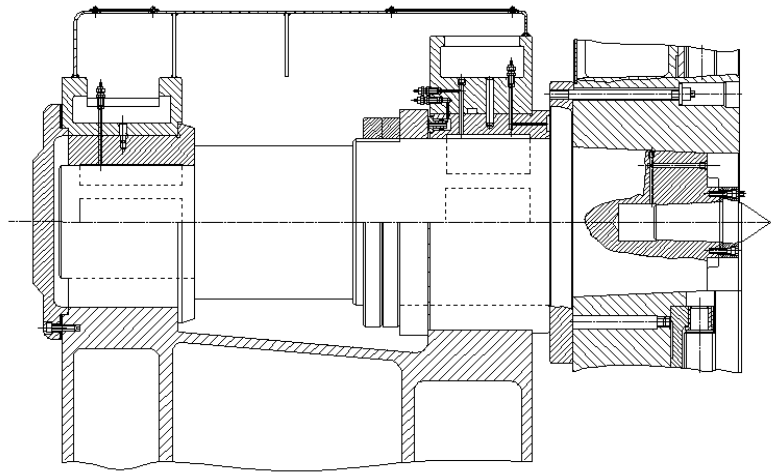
Шпиндельный узел тяжелого токарного станка с радиально-упорными гидростатическими подшипниками
